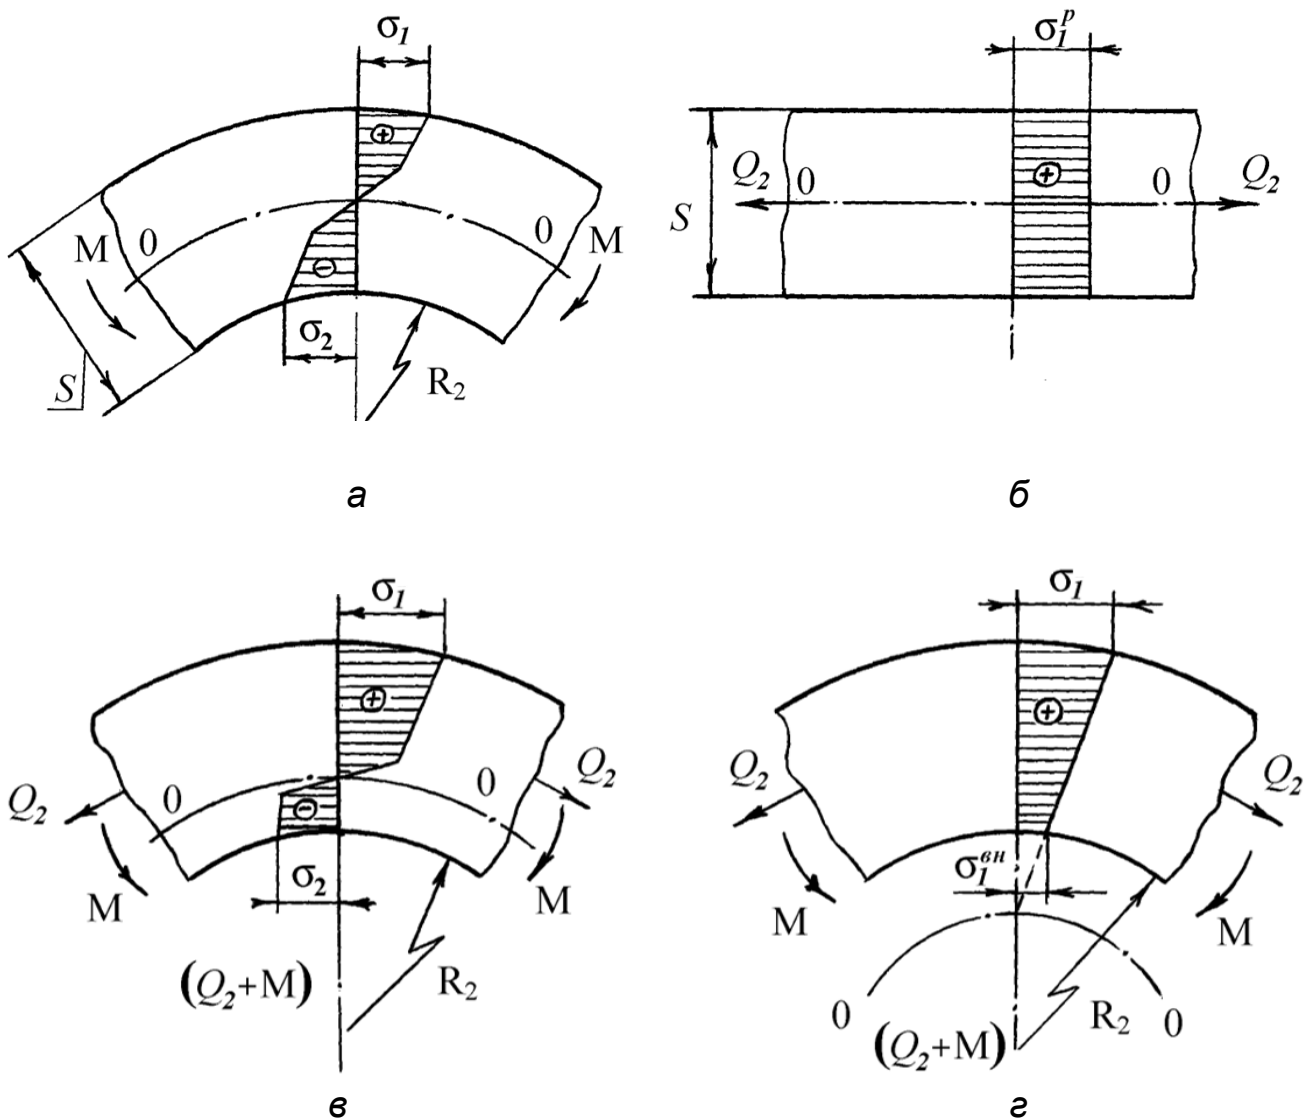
Епюри напружень у перерізі листової заготовки:
